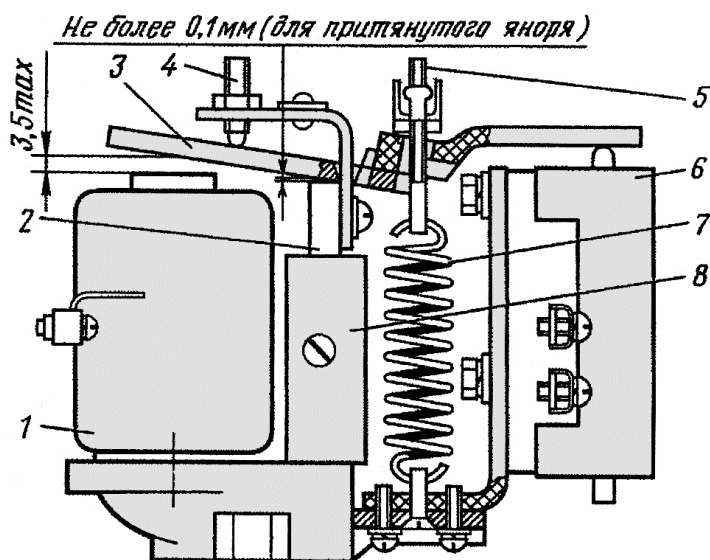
Реле времени РЭВ-292, РЭВ-294: 1 - катушка; 2 - магнитопровод; 3 - якорь; 4,5 - регулировочные шпильки; 6 - блок контактов; 7 - пружина; 8 - втулка медная
